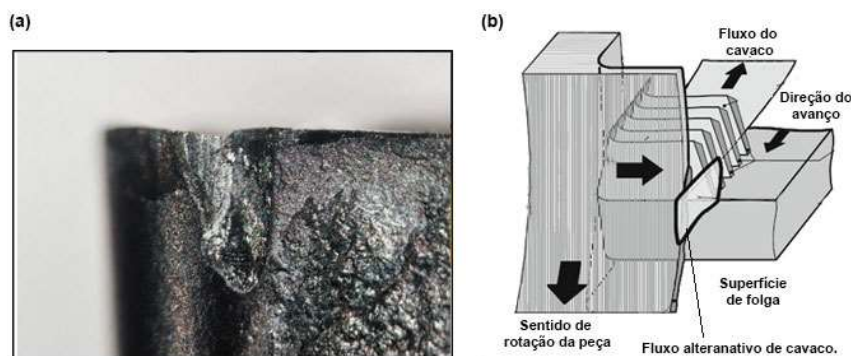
(a) ferramenta com desgaste de entalhe; (b) Ilustração esquemática de motivos que causam desgaste entalhe na aresta principal. Fonte: Klocke, 2011 - Imagem adaptada
